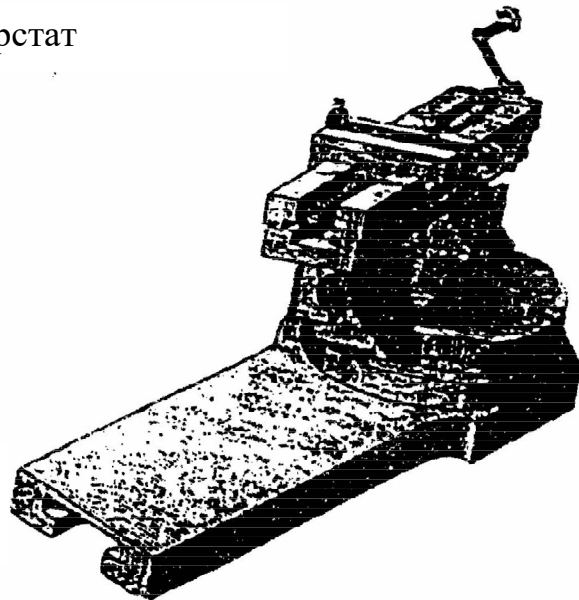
Хрестовий супорт токарного верстата (1772 р.)
